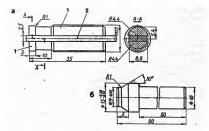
Съемник (а) для распылителя и оправка (б) для его запрессовки: 1 — половины съемника; 2 — вставка.
